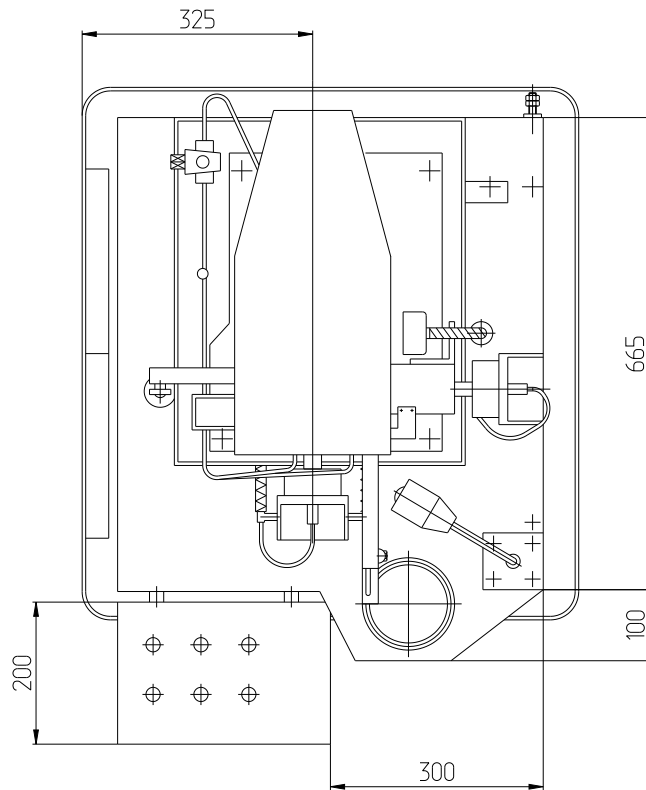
Загальний вигляд п верстата (вид з верзу)
